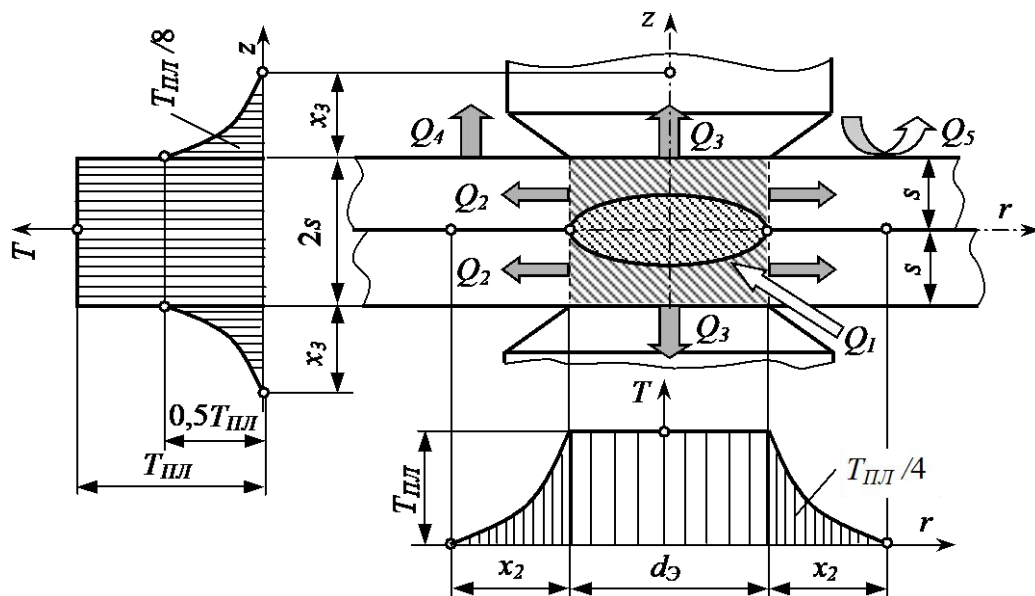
Схеми теплопередачі у зоні зварювання
